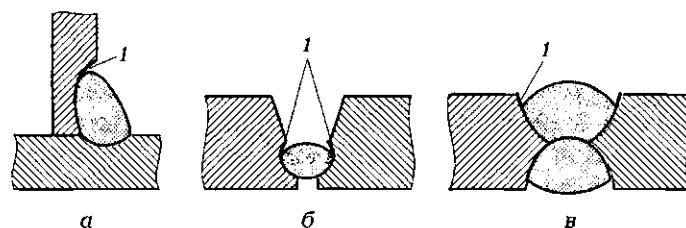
Подрезы 1 зоны сплавления в угловом (а) и стыковых одностороннем (б) и двустороннем (в) сварных швах
